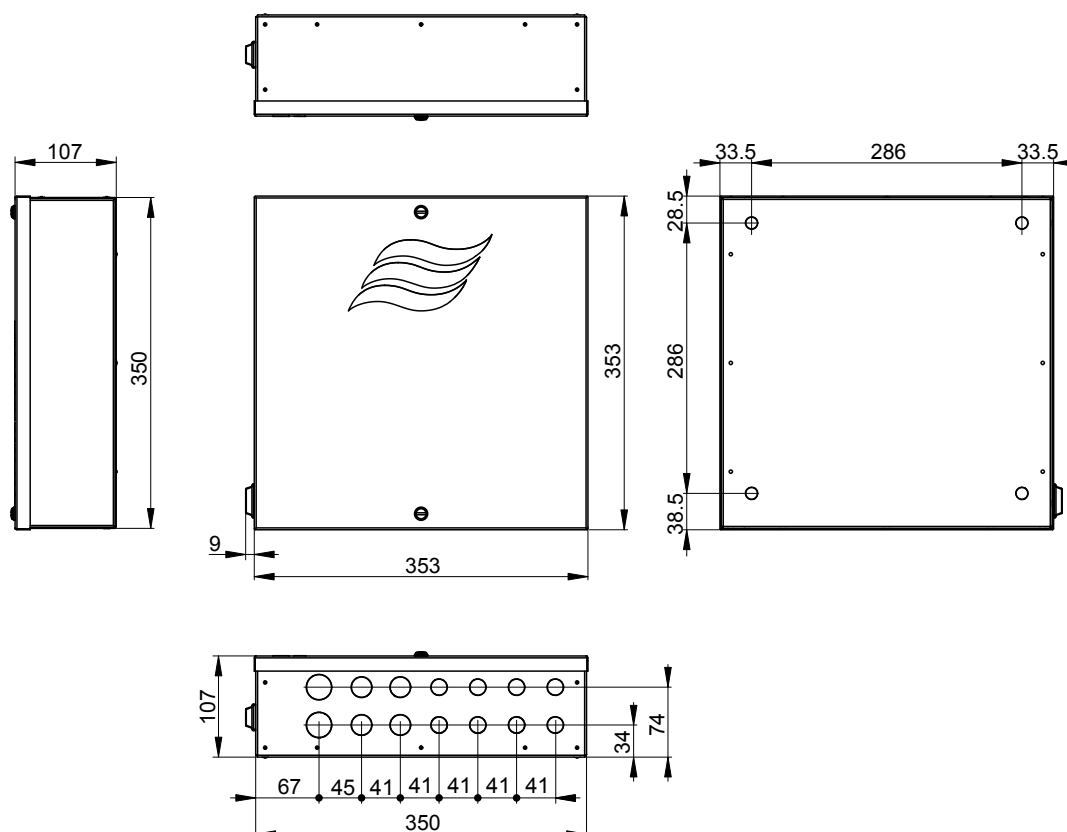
Masszeichnung Condair Delta SPA Control Box (Dimensionen in mm)
